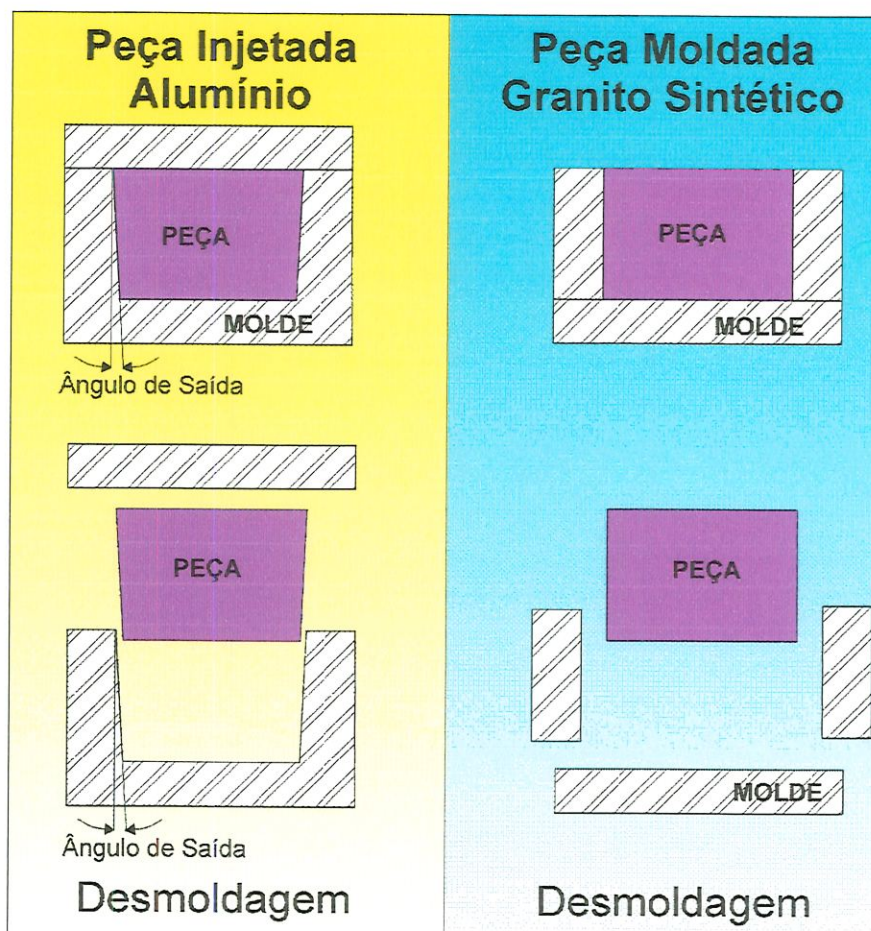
Características de desmoldagem de peças injetadas e de granito sintético.
